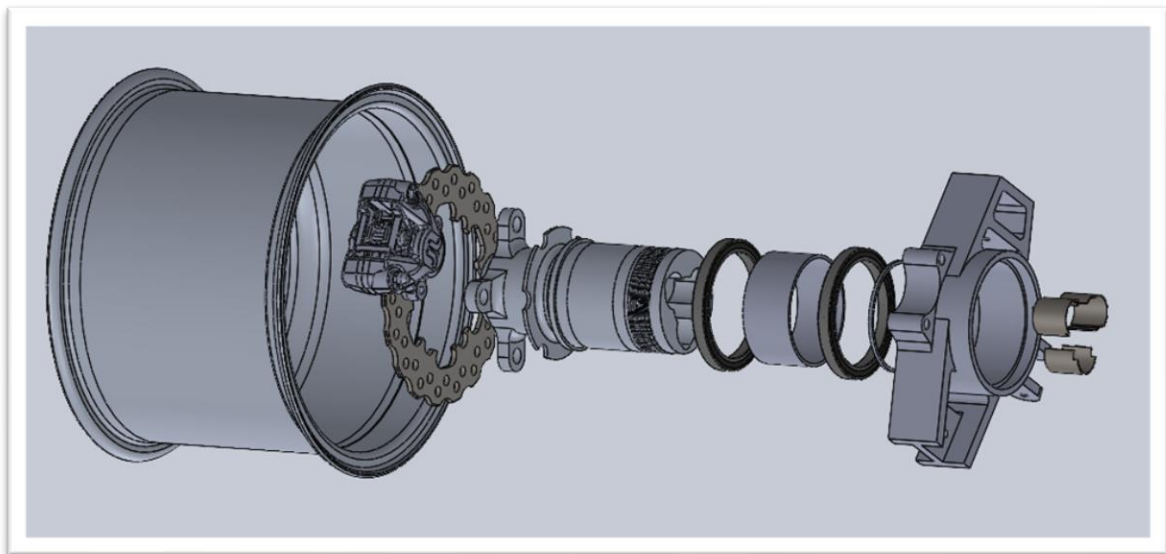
Vista explosionada del conjunto de las ruedas traseras (Vista 3D)
